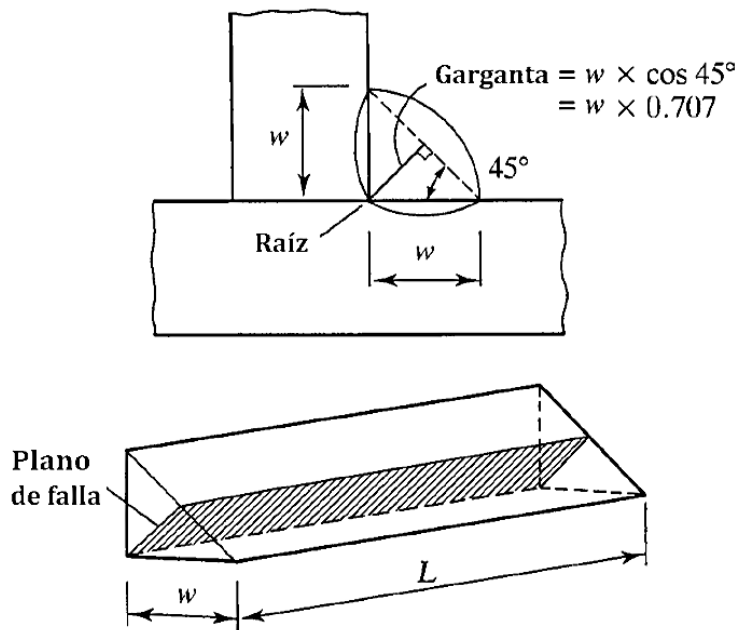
Sección transversal típica de una soldadura de filete
